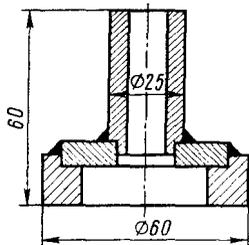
Сварная деталь с двумя круговыми швами
